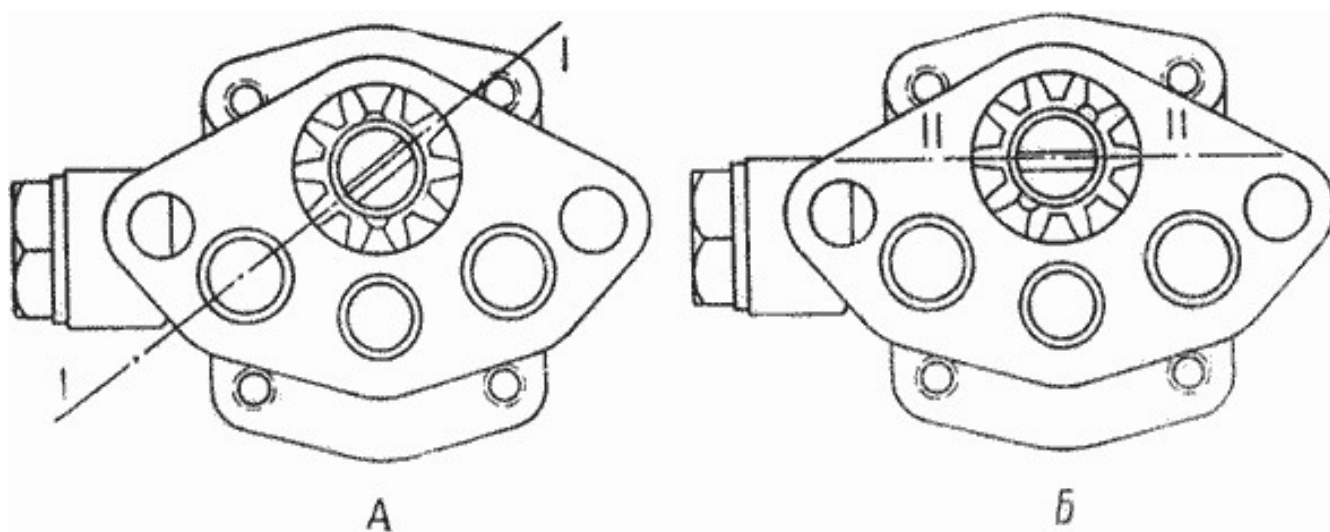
Установка валика масляного насоса (вид на валик сверху)
